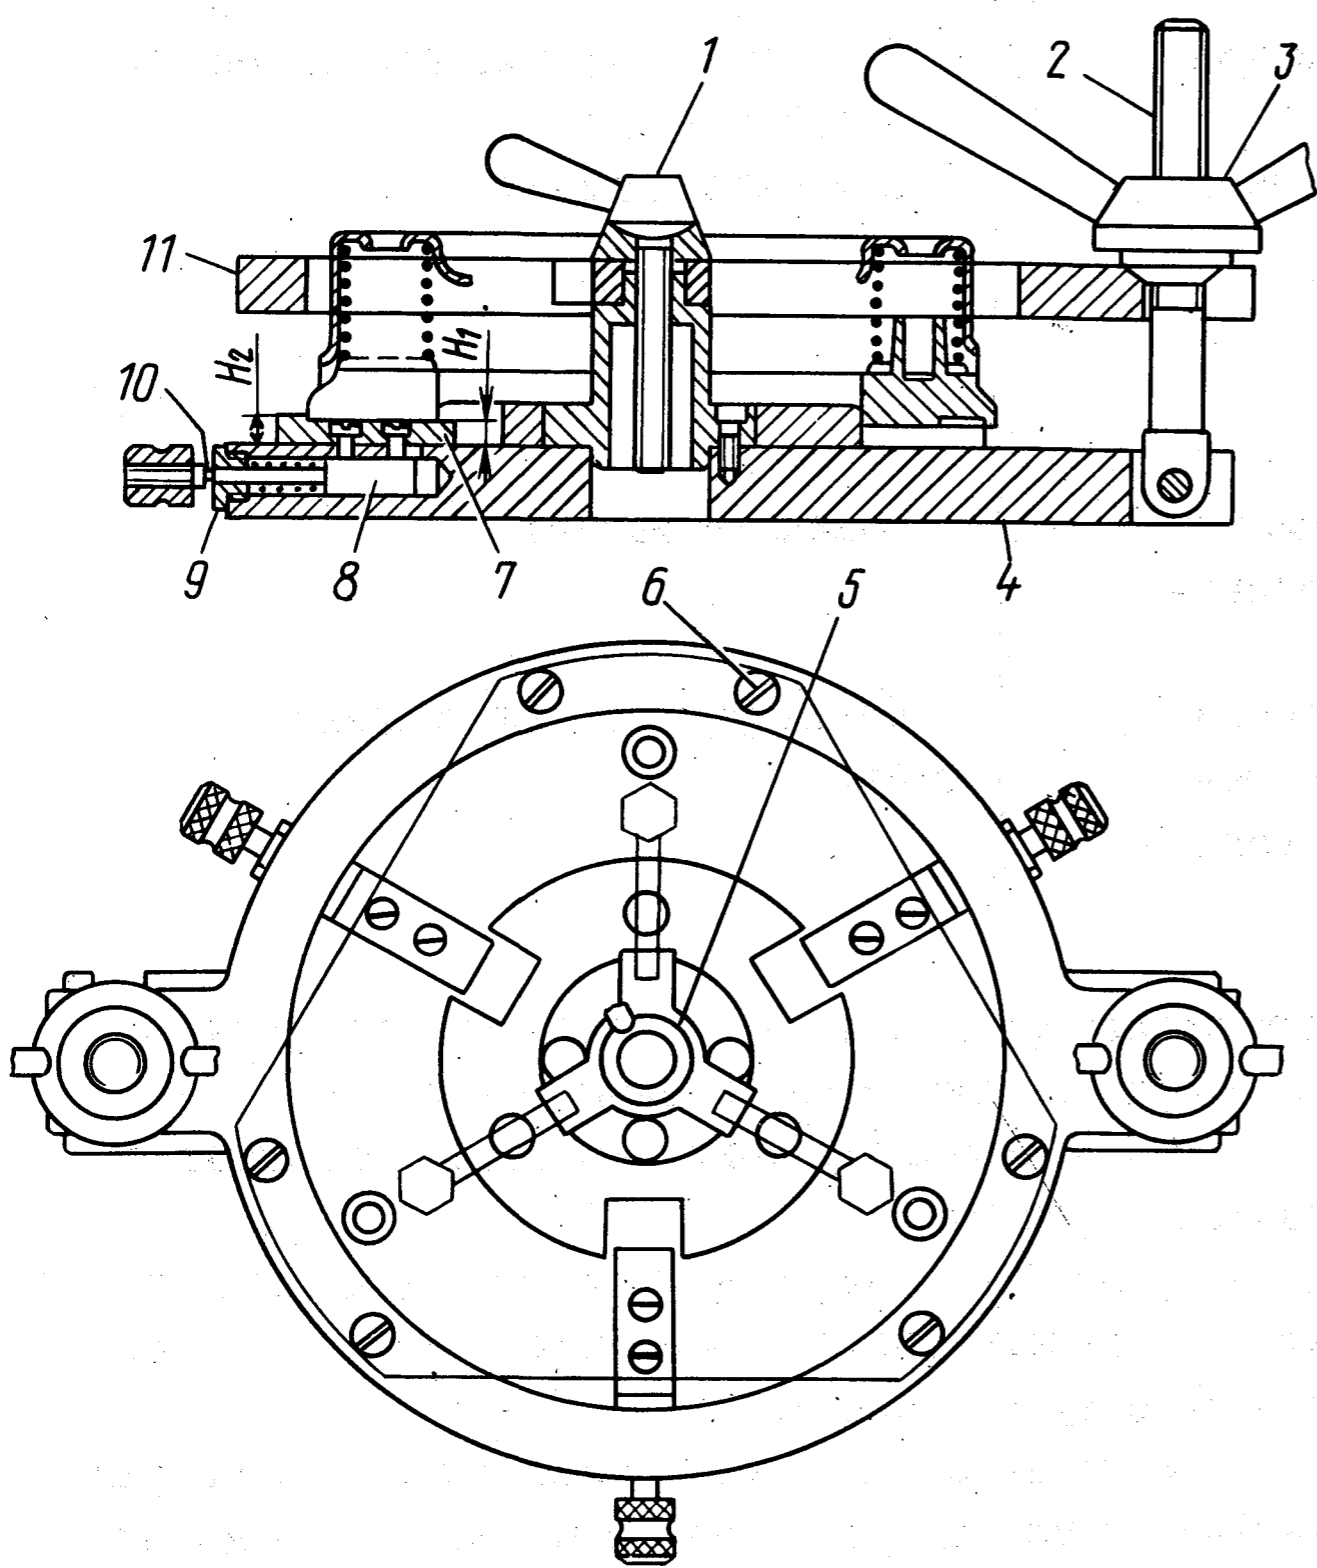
Приспособление 7820-5079 для разборки и сборки ведущего диска сцепления:
